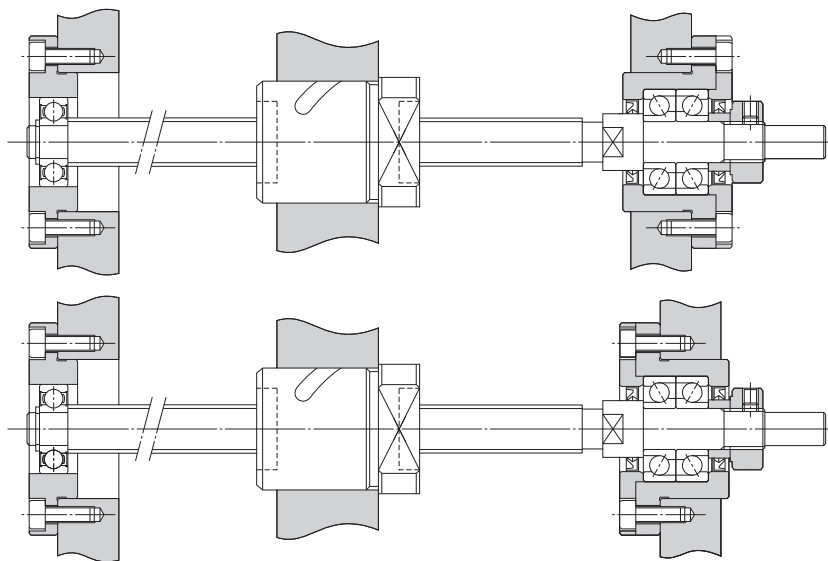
Пример установки концевой подшипниковой опоры круглого типа
